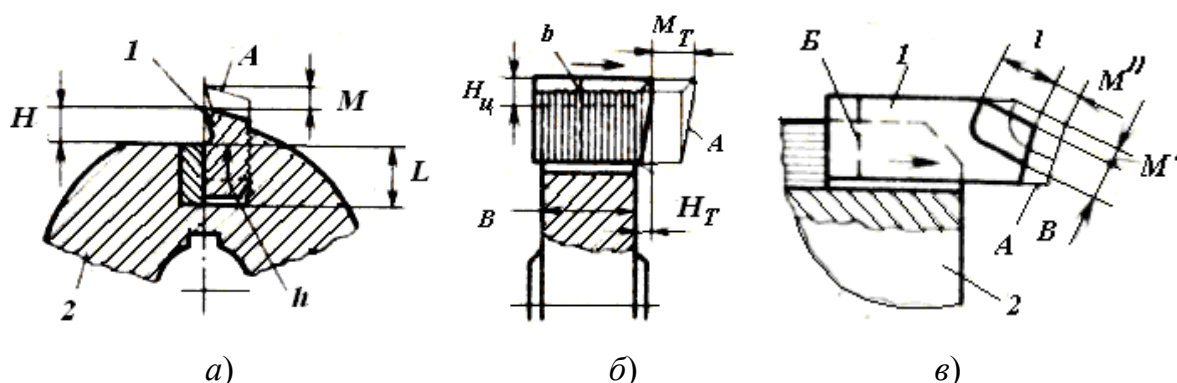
Схема определения допустимого стачивания зубьев сборных фрез
